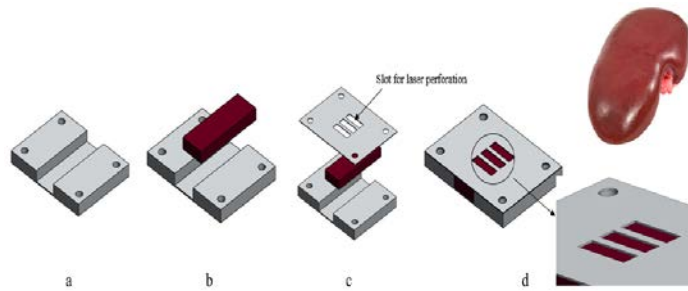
Подготовка образца биоткани. А – металлическая платформа для фиксации образца, В - металлическая платформа с образцом, С - металлическая платформа с образцом и прижимной пластиной, D - держатель образца в сборе
